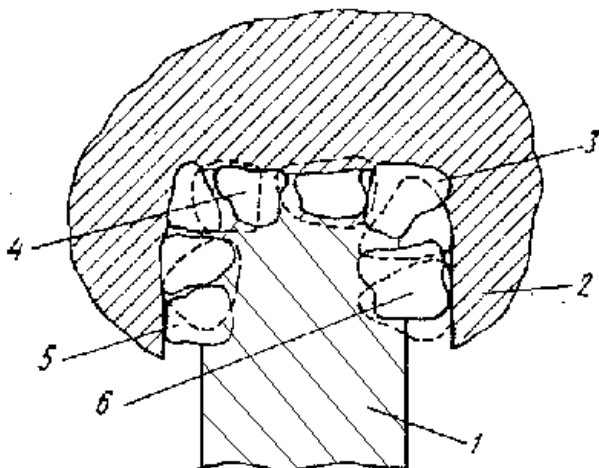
Схема расположения алмазных зерен на режущей кромке диска:
